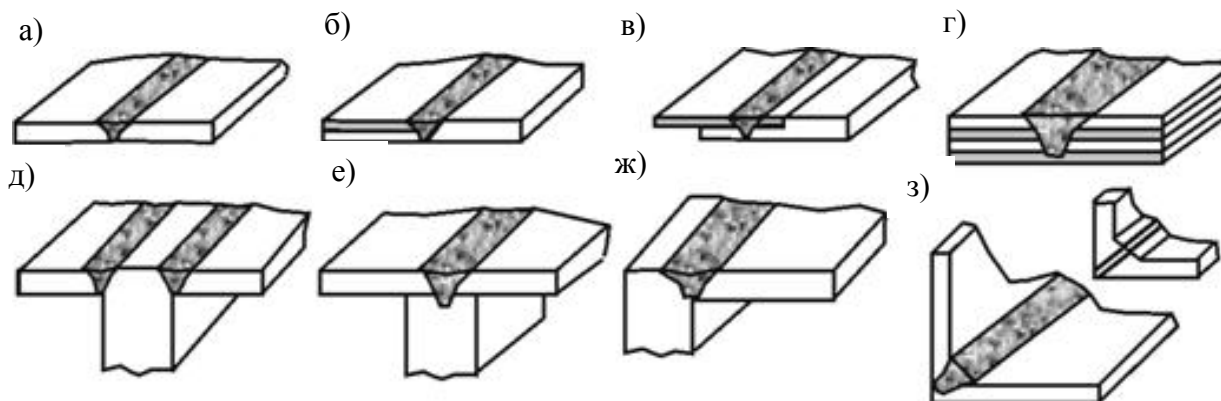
Типы сварных соединений, выполняемых СТП: а – стыковое; б – нахлесточно-стыковое; в – нахлесточное; г – многослойное нахлесточное; д – двухпроходное тавровое; е – тавровое прорезное; ж, з – угловое
